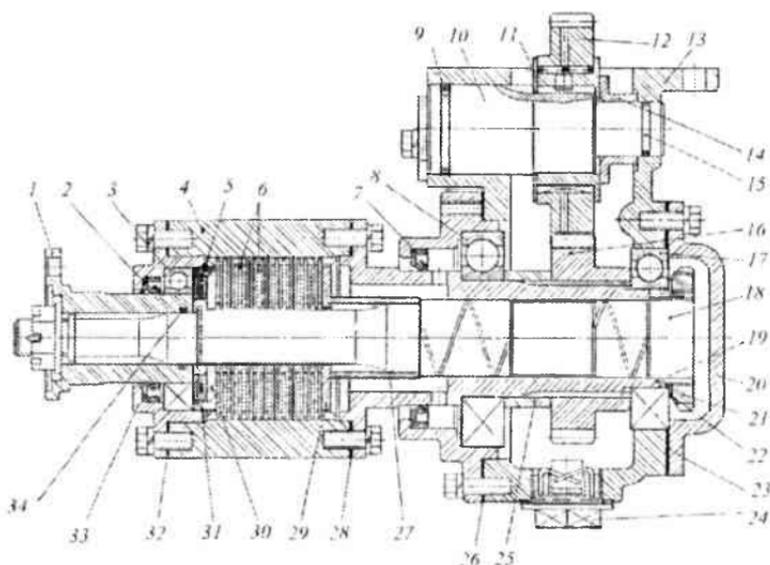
Редуктор раздаточный: 1 – фланец; 2, 7 – сальники; 3, 8, 17 – подшипники; 4 – втулка; 5 – пружина тарельчатая; 6 – диски ведомый и ведущий; 9, 15, 34 – кольца уплотнительные; 10 – ось паразитной шестерни; 11 – шайба; 12 – шестерня паразитная; 13 – корпус редуктора; 14 – втулка; 16 – шестерня ведомая; 18 – вал; 19 – вал редуктора ведомый; 20 – крышка; 21 – гайка; 22 – шайба стопорная; 23, 26, 28, 32 – прокладки; 24 – пробка спускная; 25, 27 – втулка распорная; 29, 30 – диски; 31 – втулка; 33 – стакан
